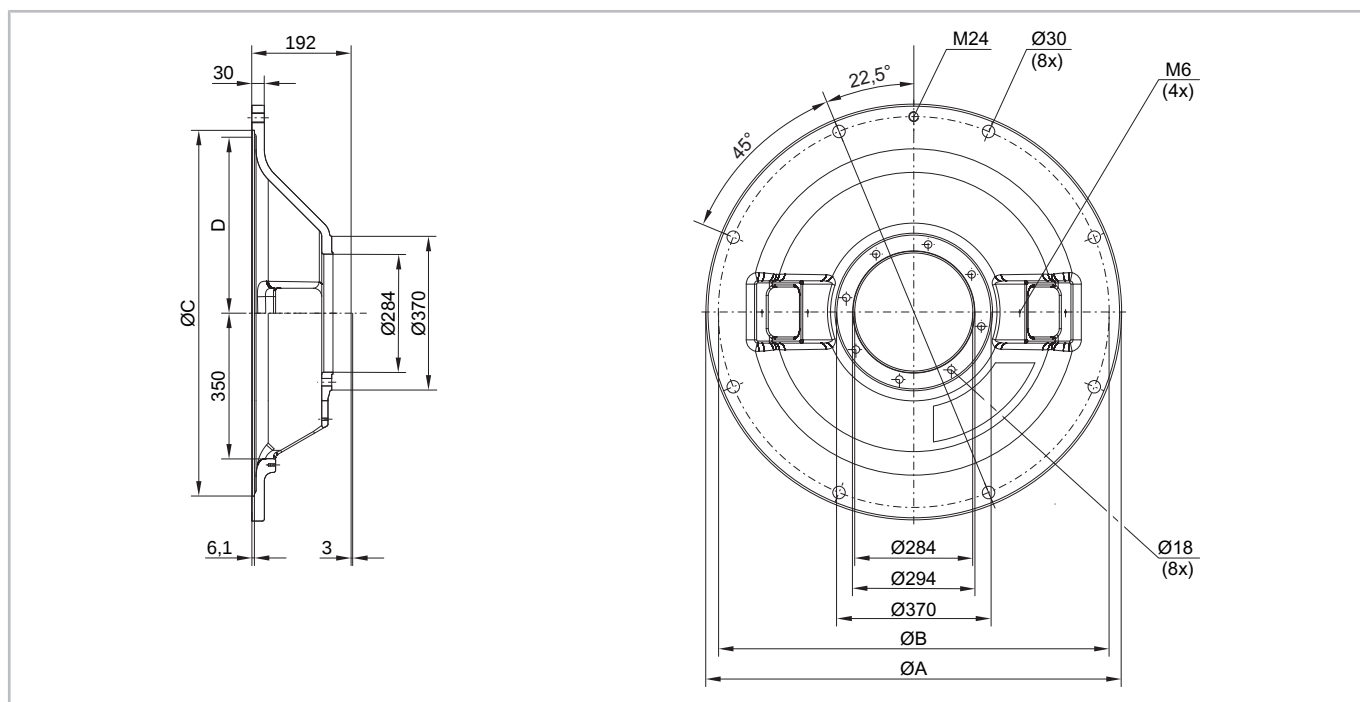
Габаритный чертеж кожуха муфты GS10100
